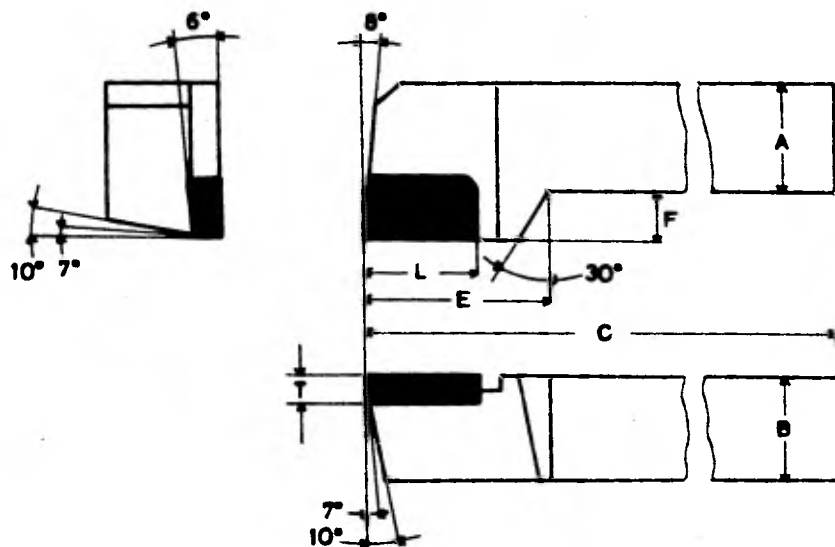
BURIL PARA TORNEADO CERCANO AL CHUCK.
